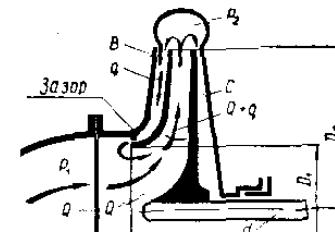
Схема протекания воды в рабочем колесе и в зазоре между колесом и крышкой корпуса.
